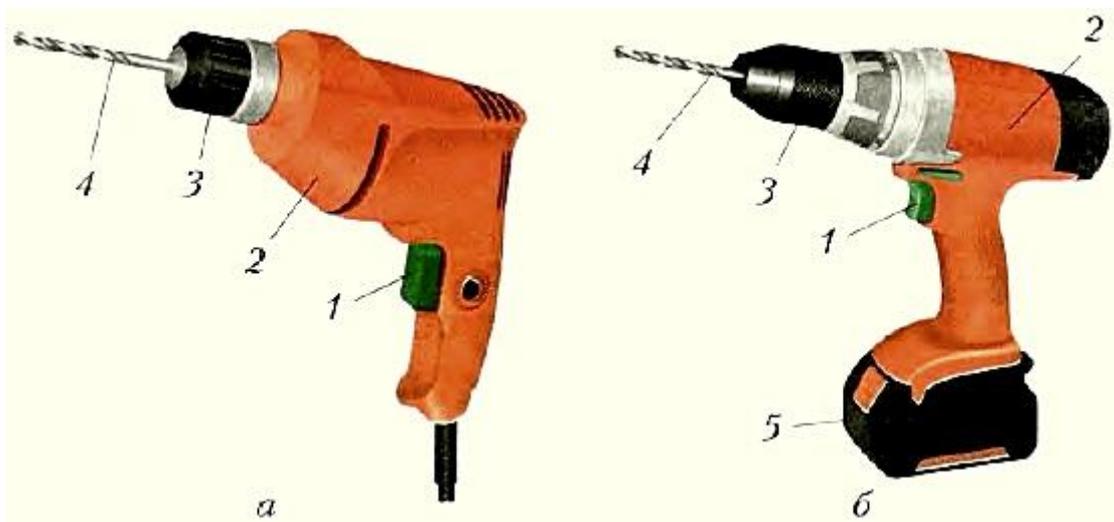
Электродрель (а) и аккумуляторная дрель-шуруповёрт (б): 1 — кнопка включения; 2 — электродвигатель в корпусе; 3 — патрон; 4 — сверло; 5 — корпус с аккумулятором
